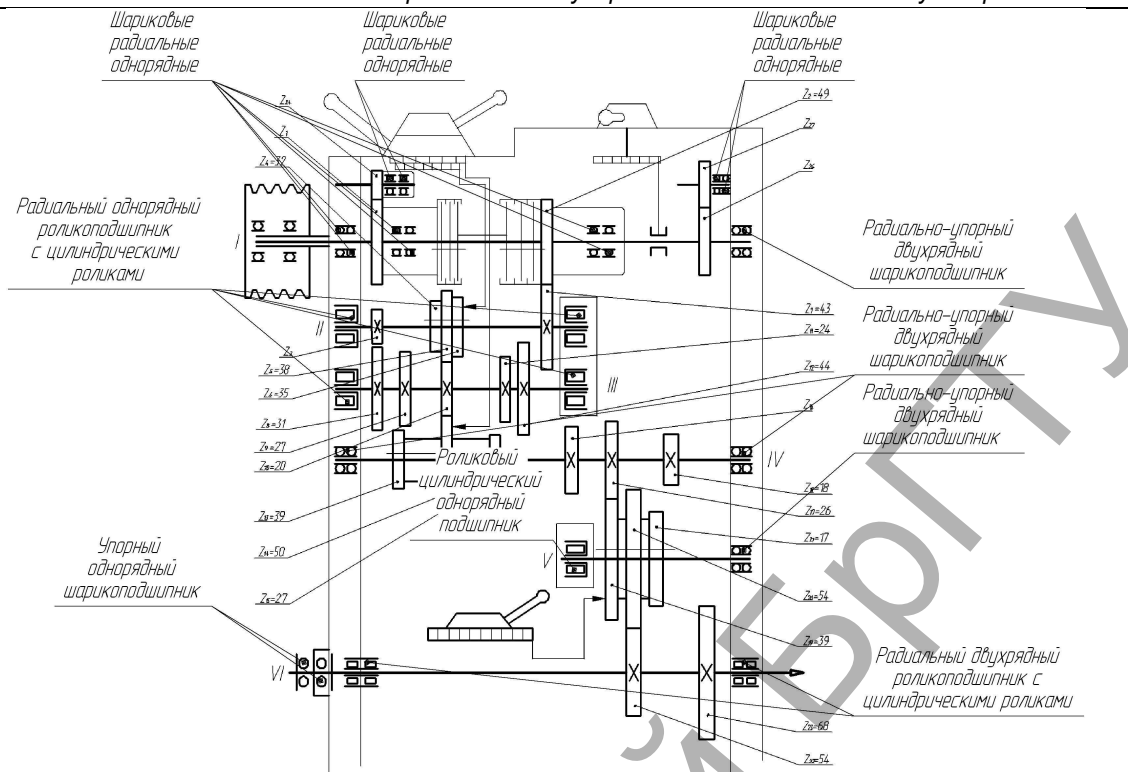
Кинематическая схема коробки скоростей универсального токарного станка СН-401/501 с обозначением типов подшипников качения
